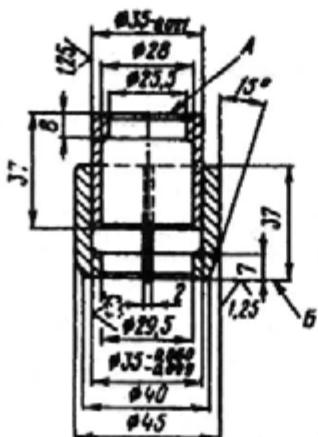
Телескопическая контрольная распорная втулка для замера расстояния между внутренними кольцами подшипников ведущей шестерни
